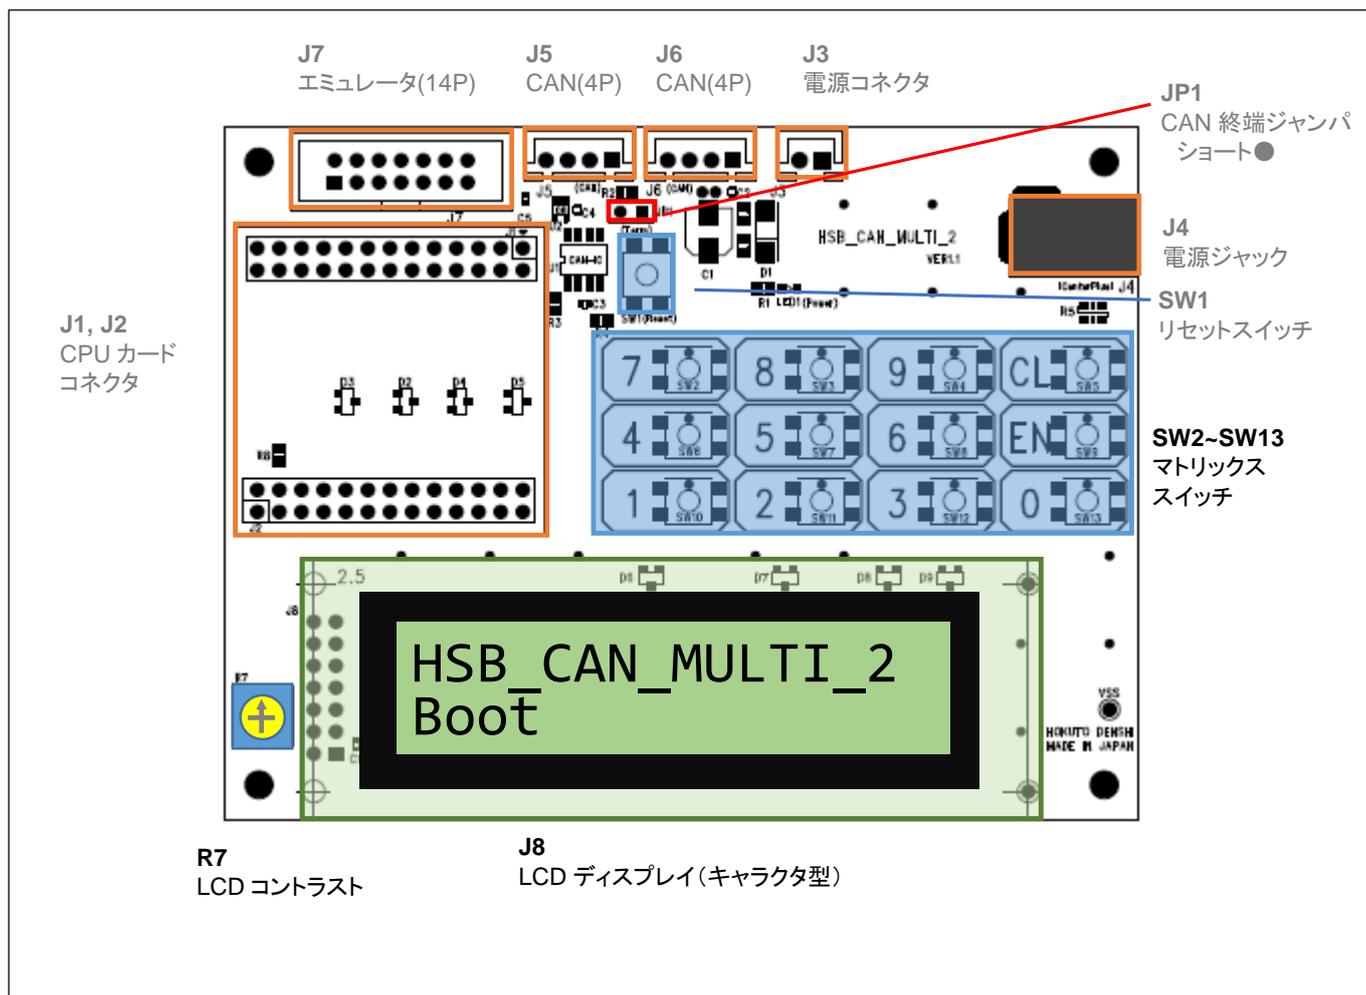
HSB CAN MULTI 2 ボード配置図
